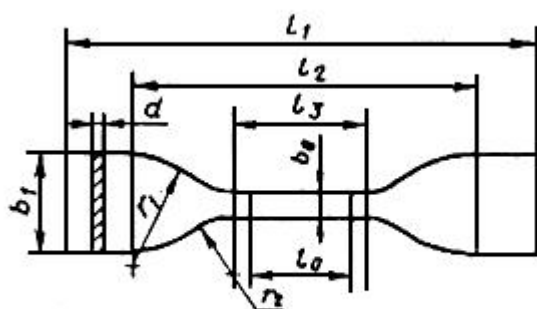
Образец формы двухсторонней лопатки согласно ГОСТ 270-75
